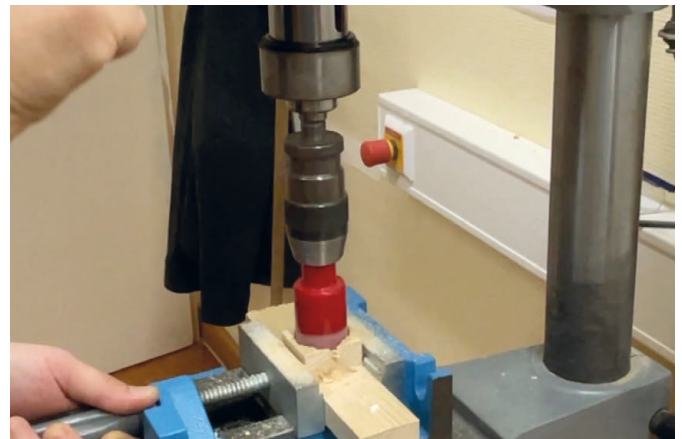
Bohren des Holzrades mit einer Lochsäge
